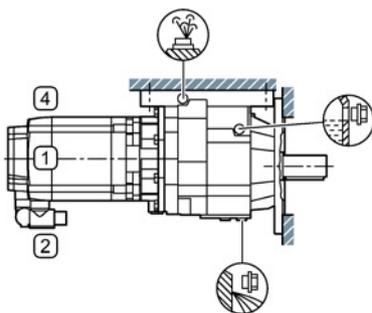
Einbaulagen für Stirnradgetriebe ZB und DB, Fuß- Flanschausführung, Baugröße 29, 2-stufig und 3-stufig
